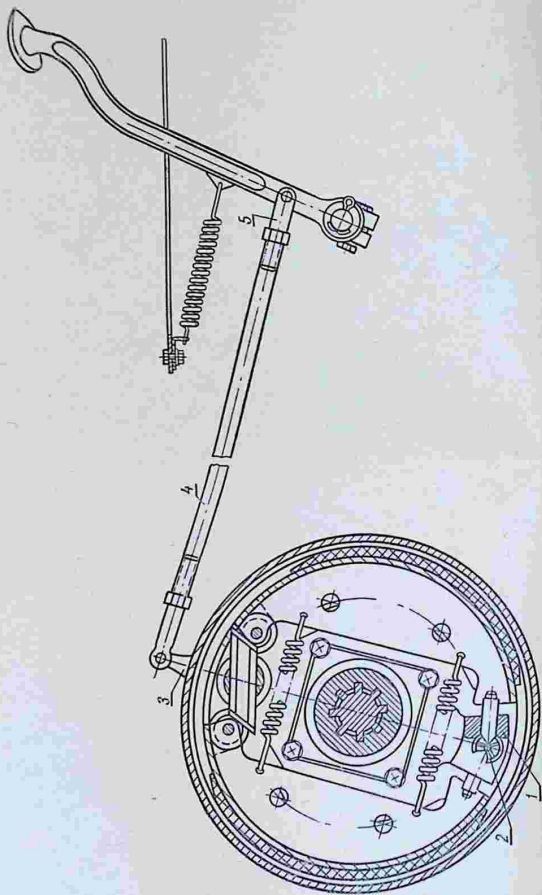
Механизм управления тормозами трактора МТЗ-5К:
